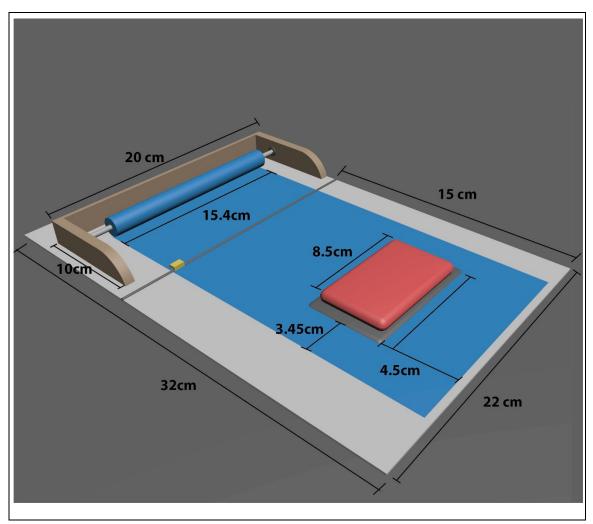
Plano de construcción de accesorio de medición y corte Poka Yoke
